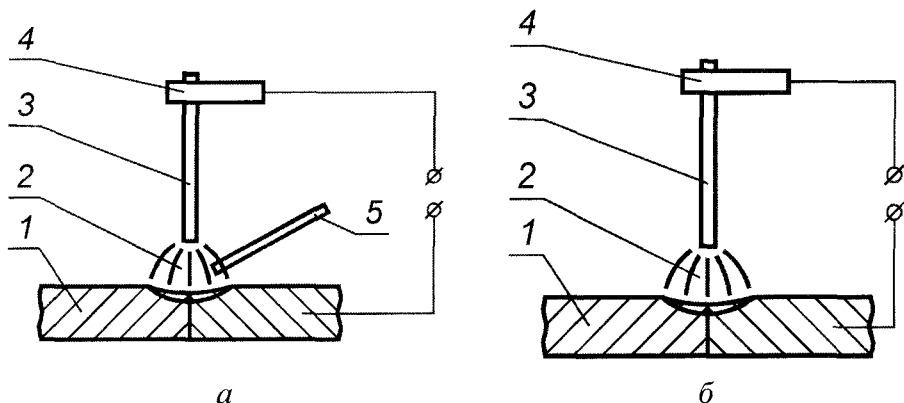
Схема ручной дуговой сварки неплавящимся (а) и плавящимся (б) электродом: 1 – свариваемый металл; 2 – электрическая дуга; 3 – электрод; 4 – электродержатель; 5 – присадочный материал
